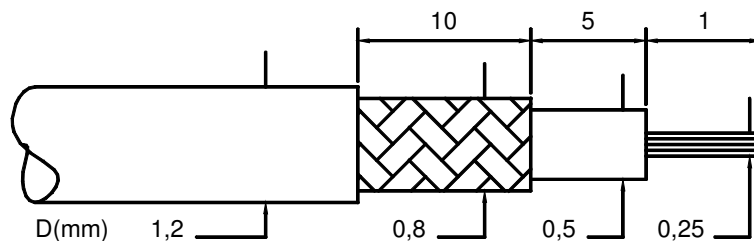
Características do cabo coaxial empregado na conexão da matriz com o meio exterior. Os diâmetros identificam o cabo, e as dimensões lineares são apropriadas para facilitar o trabalho de fixação e soldagem. Desenho fora de escala.
